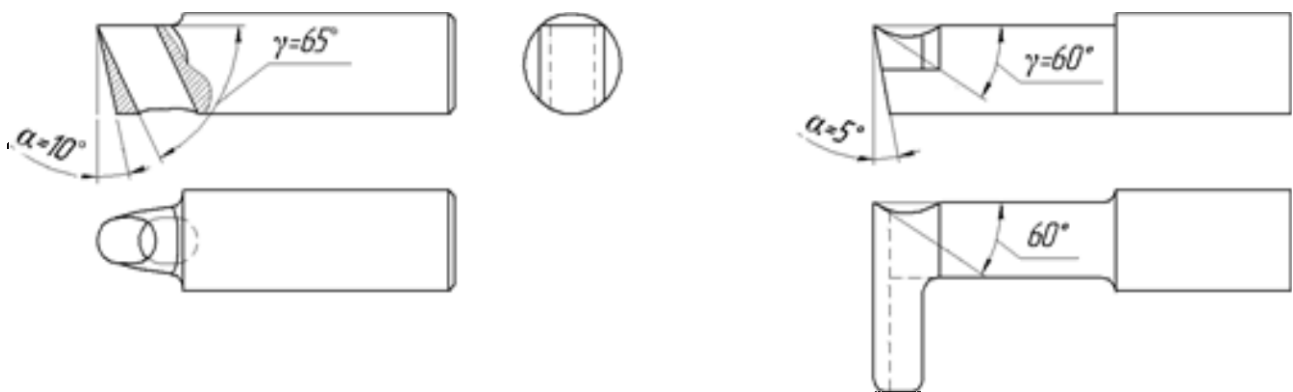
Конструкции резцов для обработки мягкой резины: с отводом стружки через отверстие в головке резца, резец с консольной головкой
